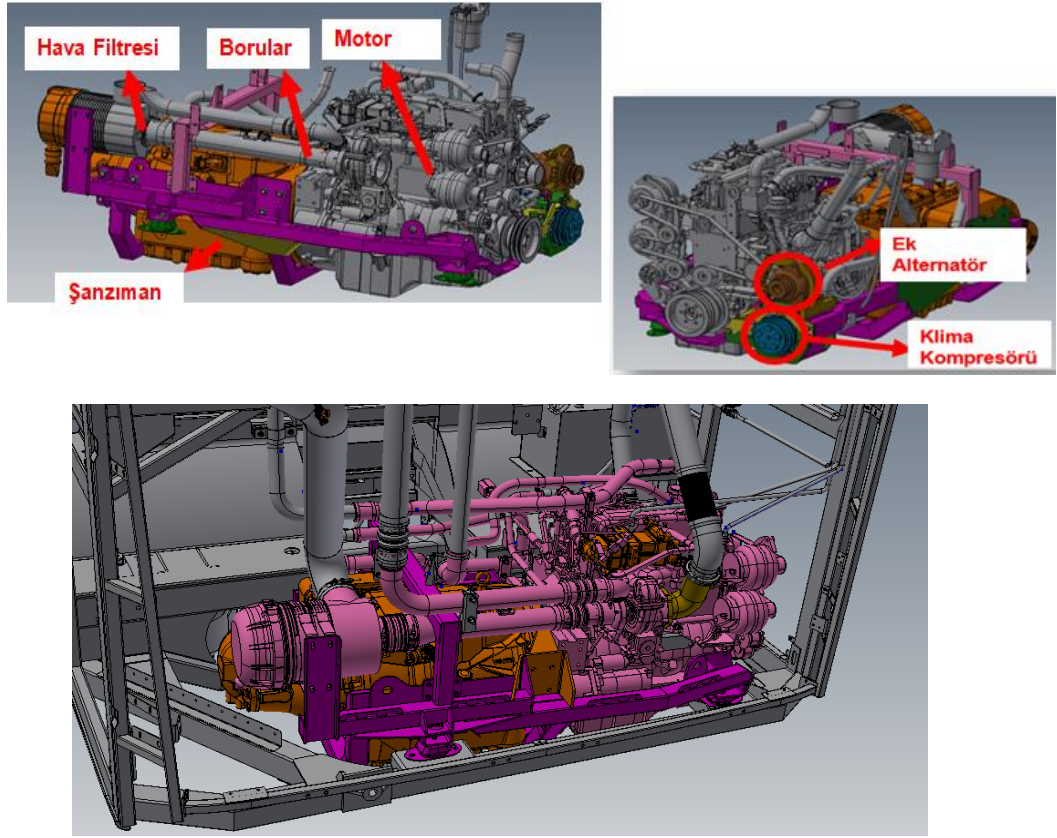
Motor ve motor beşiđi bađlantısı
